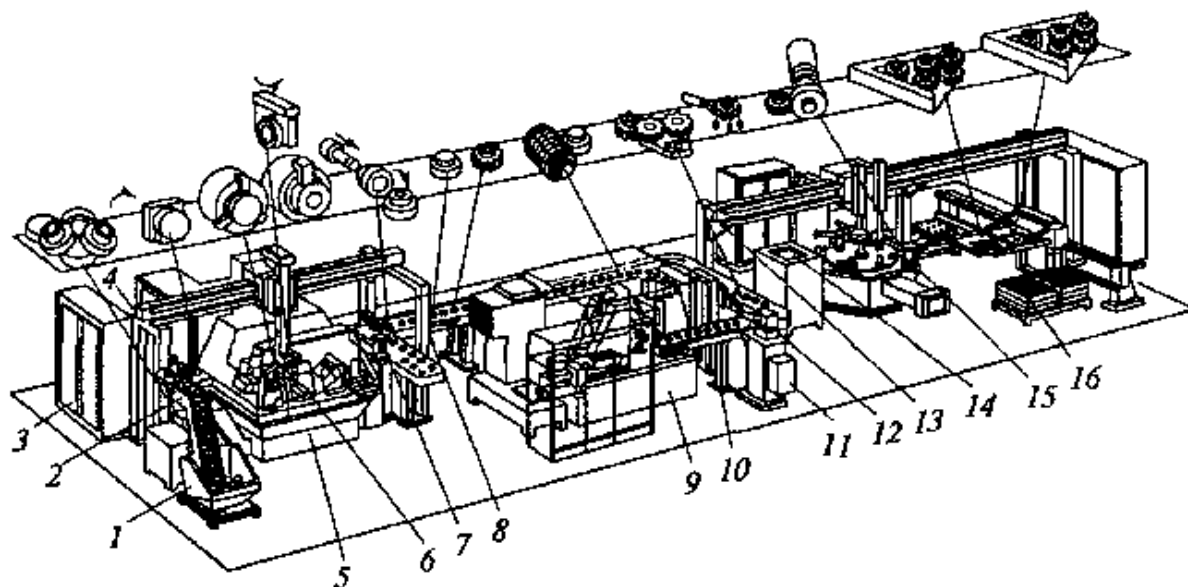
ГАЛ для обробки зубчастих коліс:
